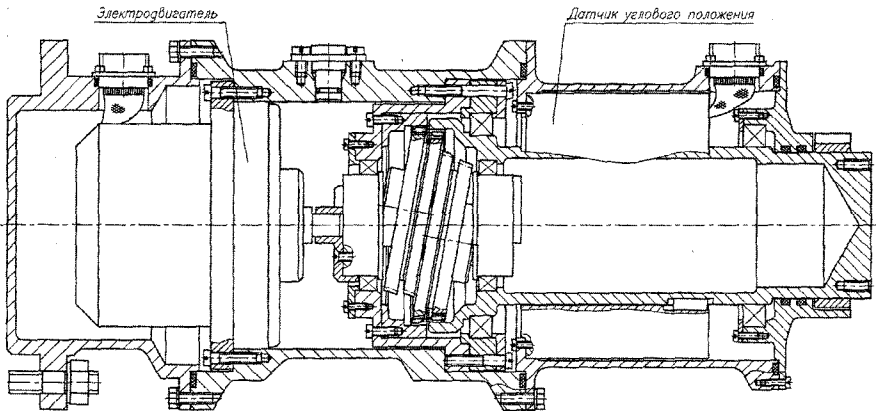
Конструкция электромеханического привода с редуктором РПНС-50
